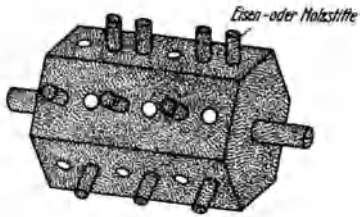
Steuerungszyylinder für Schafmaschinen (vgl. Abb. 525). Anschläge (entspr. ungelochter Karte) als einsetzbare Eisen- oder Holzstifte.
